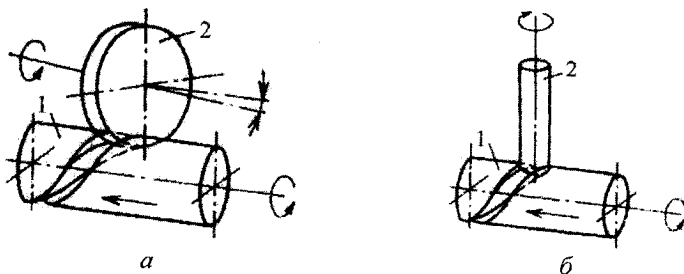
Обробка гвинтових поверхнь: *а* – дисковою фрезою; *б* – пальцевою фрезою; *1* – заготовка; *2* – інструмент
